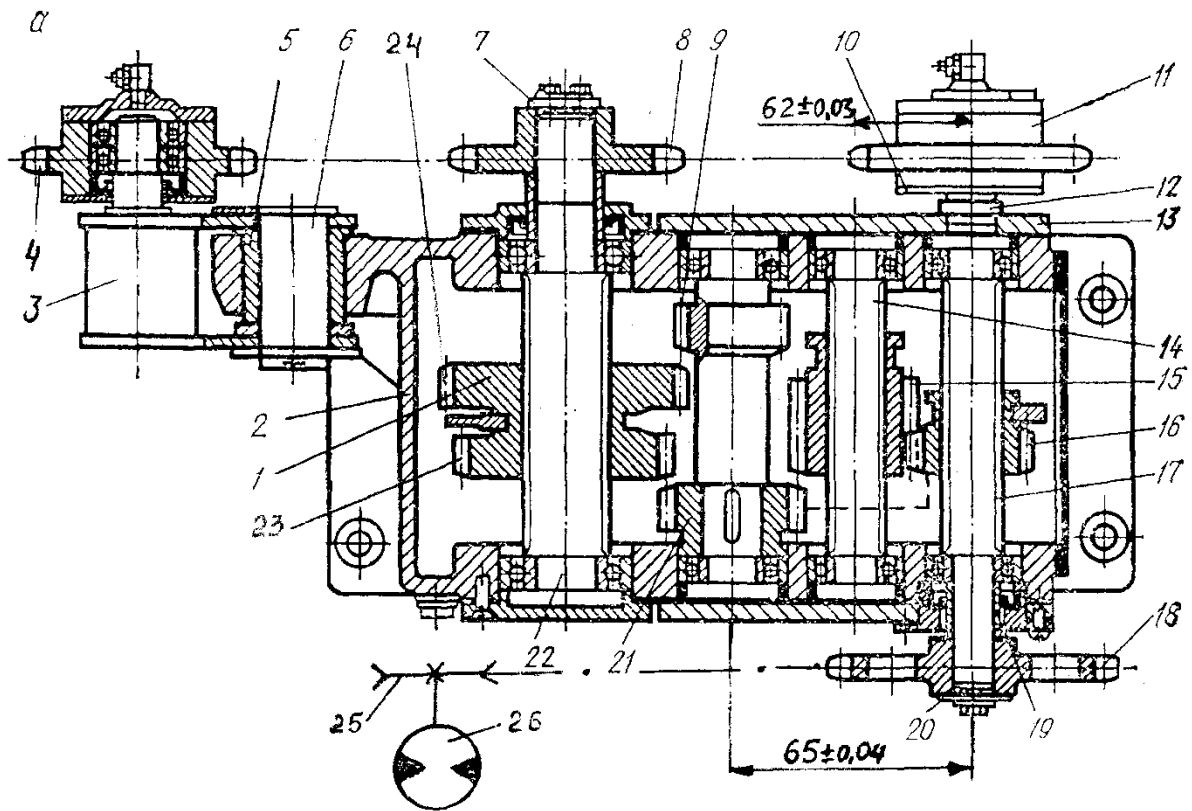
Коробка передач привода транспортера экскаватора:
